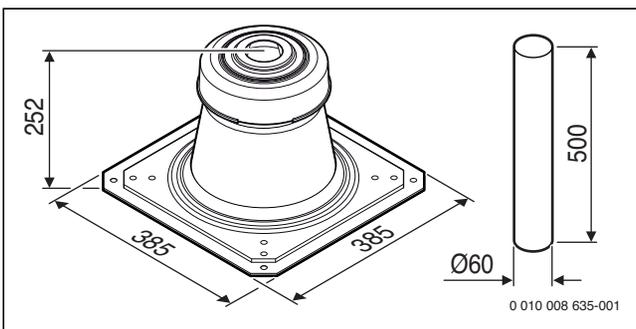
Schachtabdeckung für 60 mm, Kunststoff (Maße in mm)
